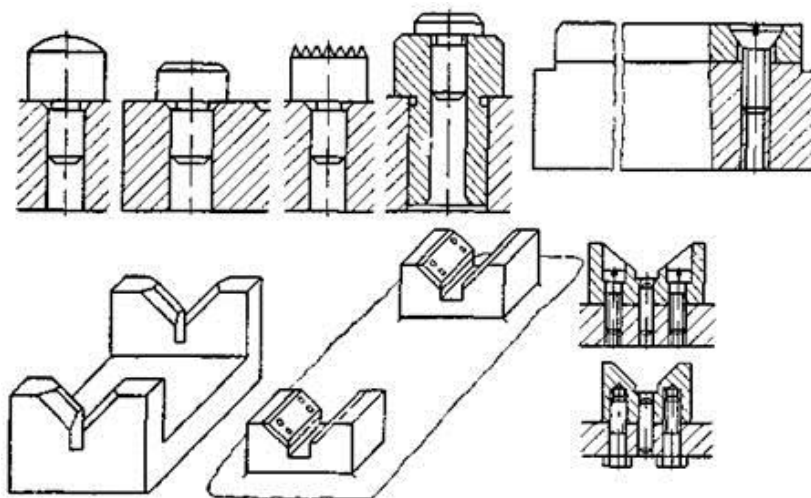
Виды установочных неподвижных опор: а – штыри; б – пластины; в – призмы
